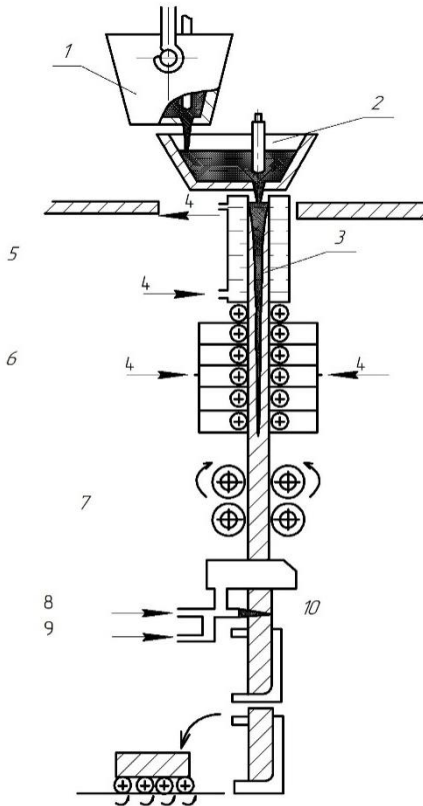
Схема установки для безпервного лиття і безпервної розливання
